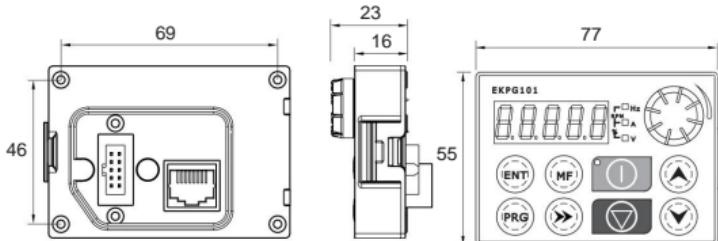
Dimensões de instalação do teclado (Unidade: mm)
